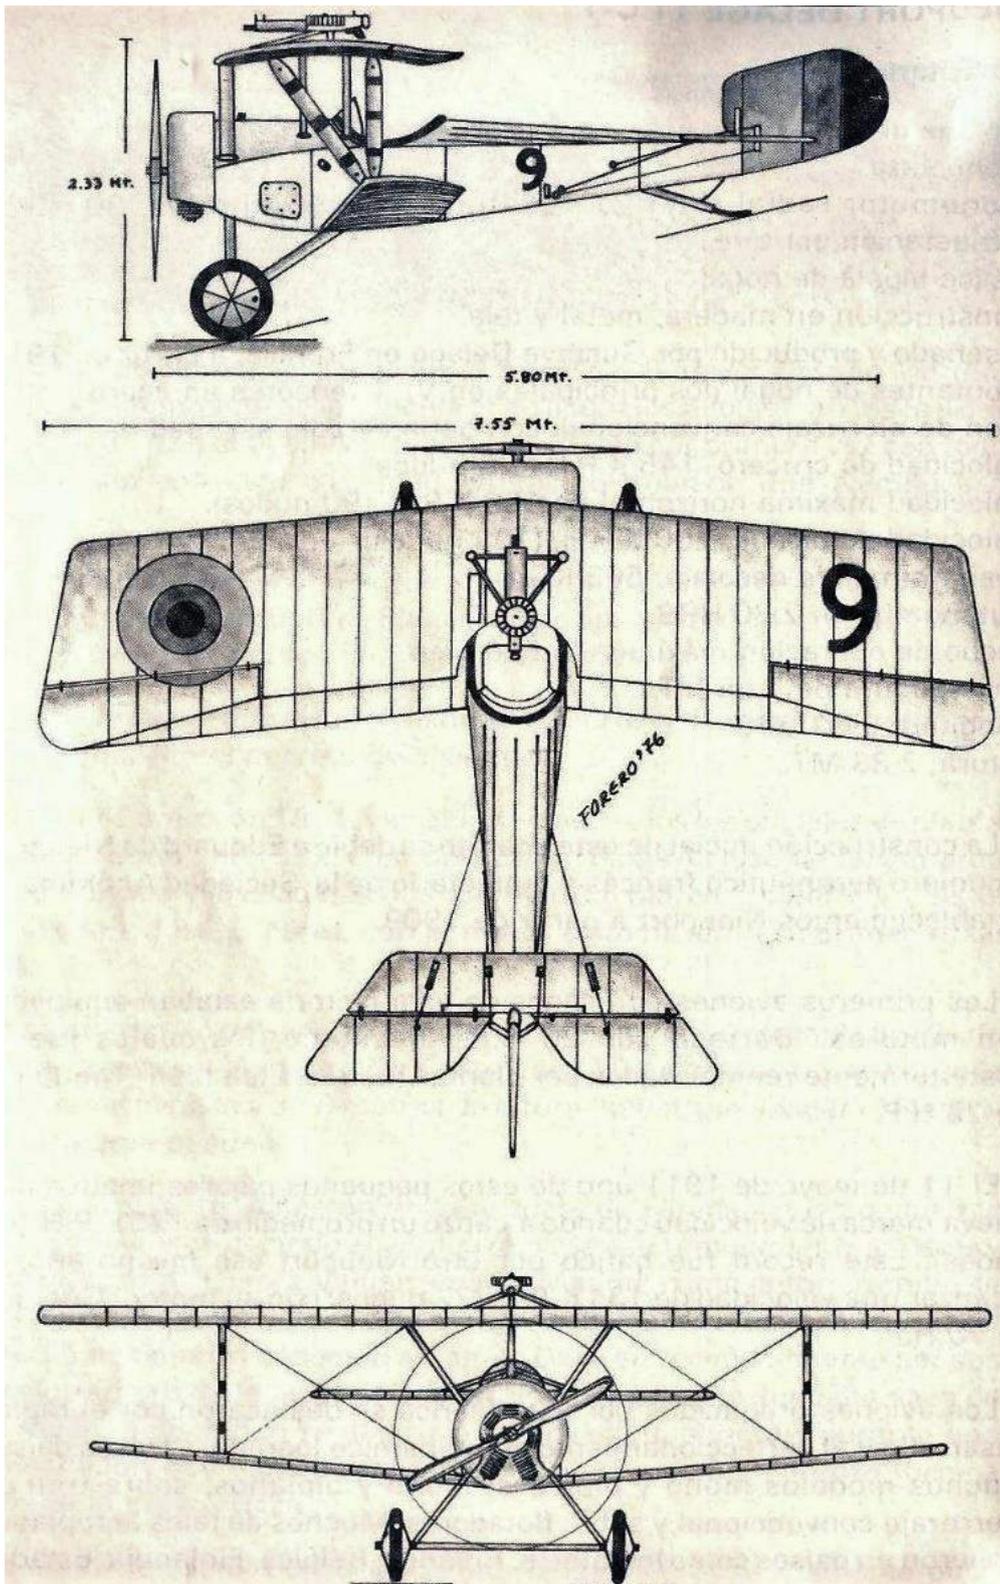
Plan d'un Nieuport Delage 11 BB
